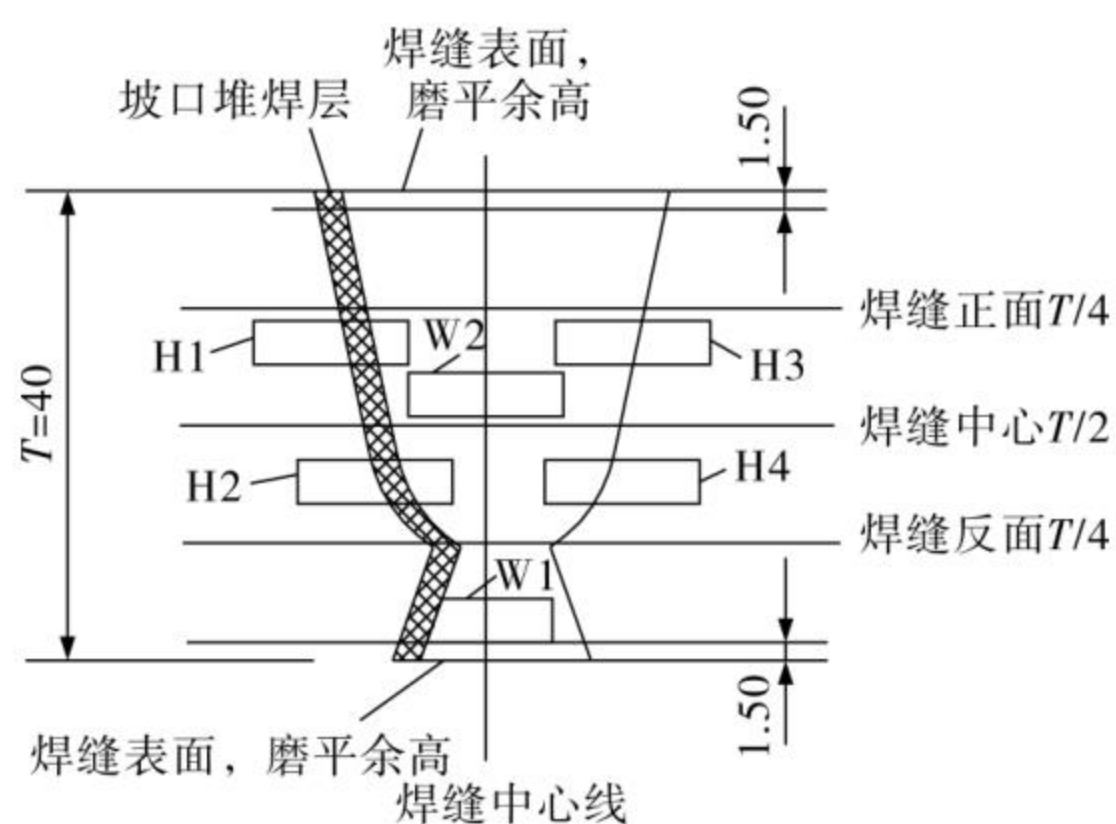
焊缝和热影响区冲击试样取样位置示图
